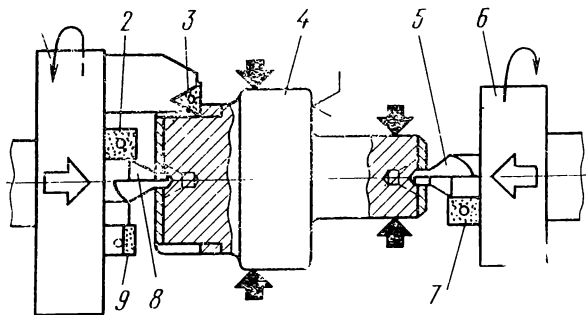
Схема фрезерования и центрования торцов колеса-вала специальными инструментальными головками
